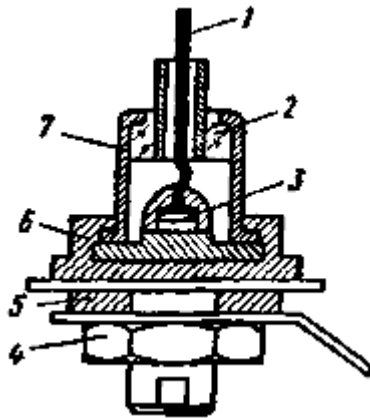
Конструкція площинного випрямного діоду: 1 – вивід; 2 – скляна втулка; 3 – напівпровідниковий кристал; 4 – гайка; 5 – шайба; 6 – основа; 7 – металевий корпус
